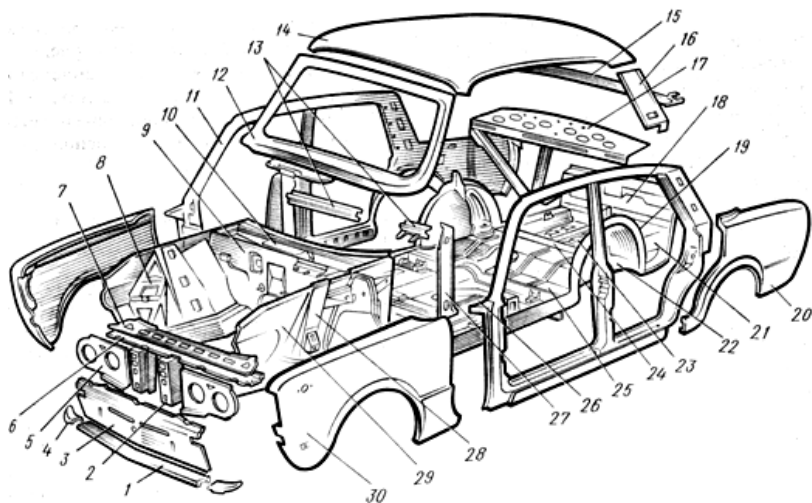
Элементы корпуса кузова ВАЗ 2103, -2106
